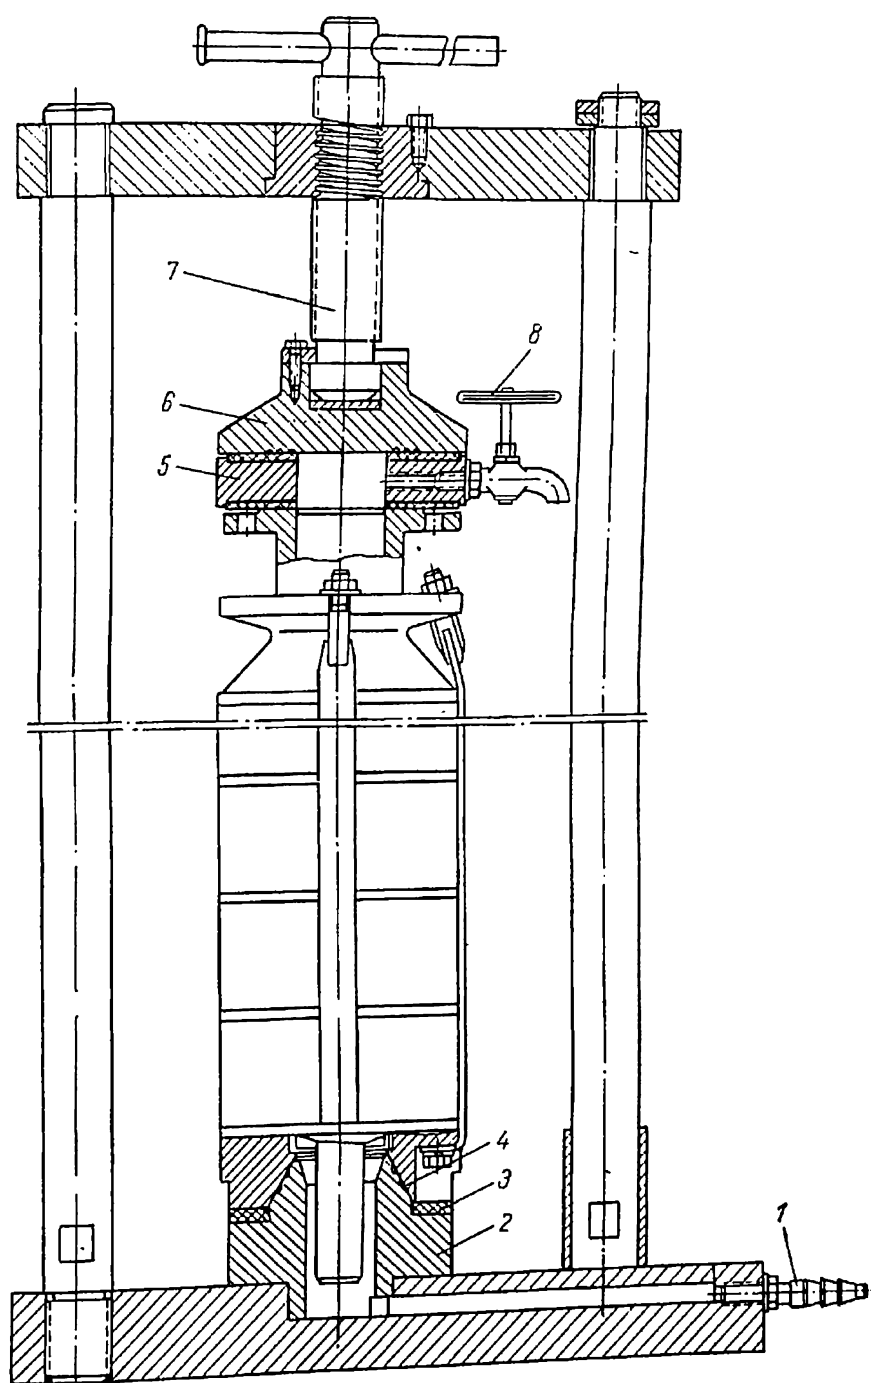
Схема установки для гидравлического испытания погружных насосов
